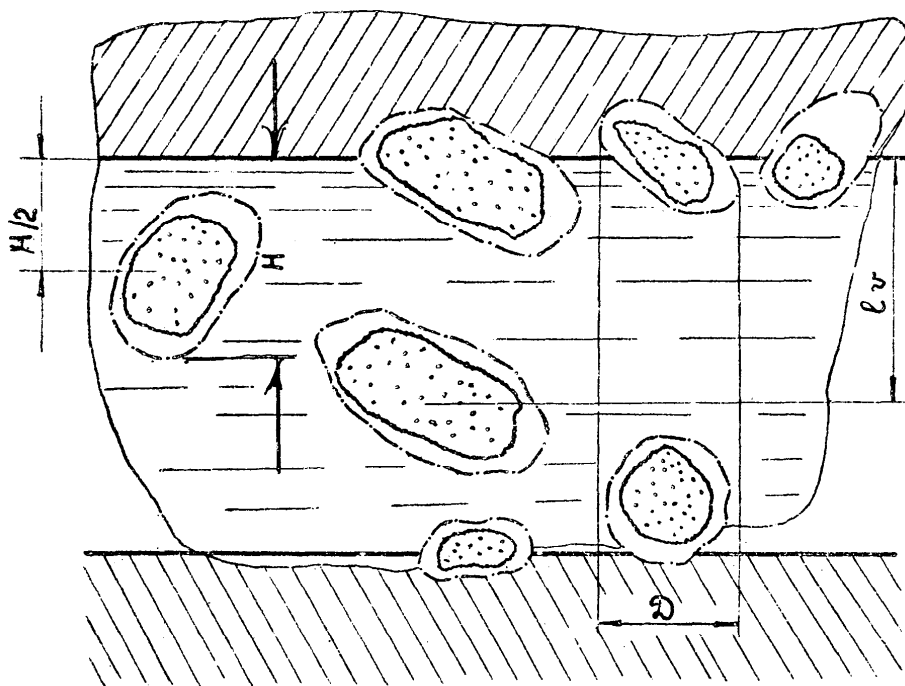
Иллюстрация к пояснению средневероятностного положения абразивного зёрна в приповерхностных слоях обрабатываемой детали и инструмента притира или сопрягаемых поверхностях арматуры
